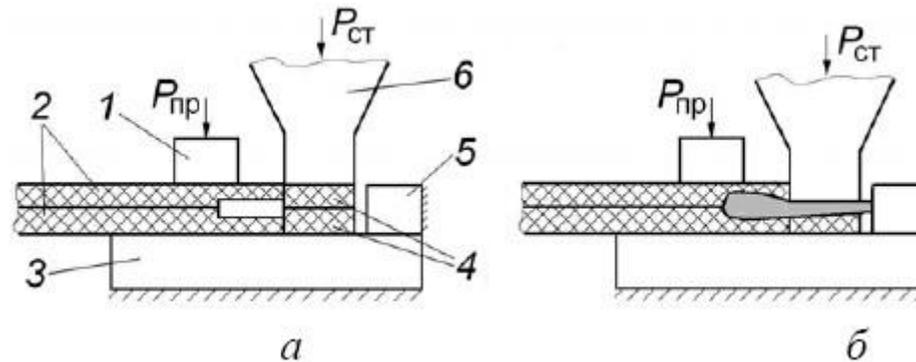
Схема ультразвуковой сварки «вытесненным расплавом»: а – перед сваркой; б – после сварки; 1 – прижим; 2 – свариваемые детали; 3 – опора; 4 - технологические детали, подвергающиеся УЗ воздействию; 5 – упор; 6 – волновод; $P_{пр}$ – давление прижима; $P_{ст}$ – статическое сварочное давление
